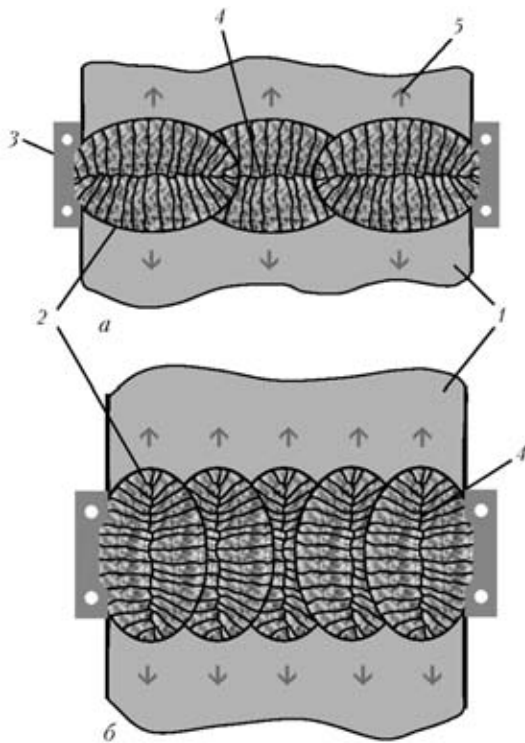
Схемы расположения зон (плоскостей) слабины в металле слоев многослойного шва при выполнении ЭШС плавящимися мундштуком с установкой плавящихся мундштуков вдоль оси разделки кромок (а) и поперек (б): 1 — свариваемая кромка; 2 — форма слоя сварного шва в поперечном сечении; 3 — формирующая накладка; 4 — зона слабины (плоскость); 5 — вектор усадочных сил
